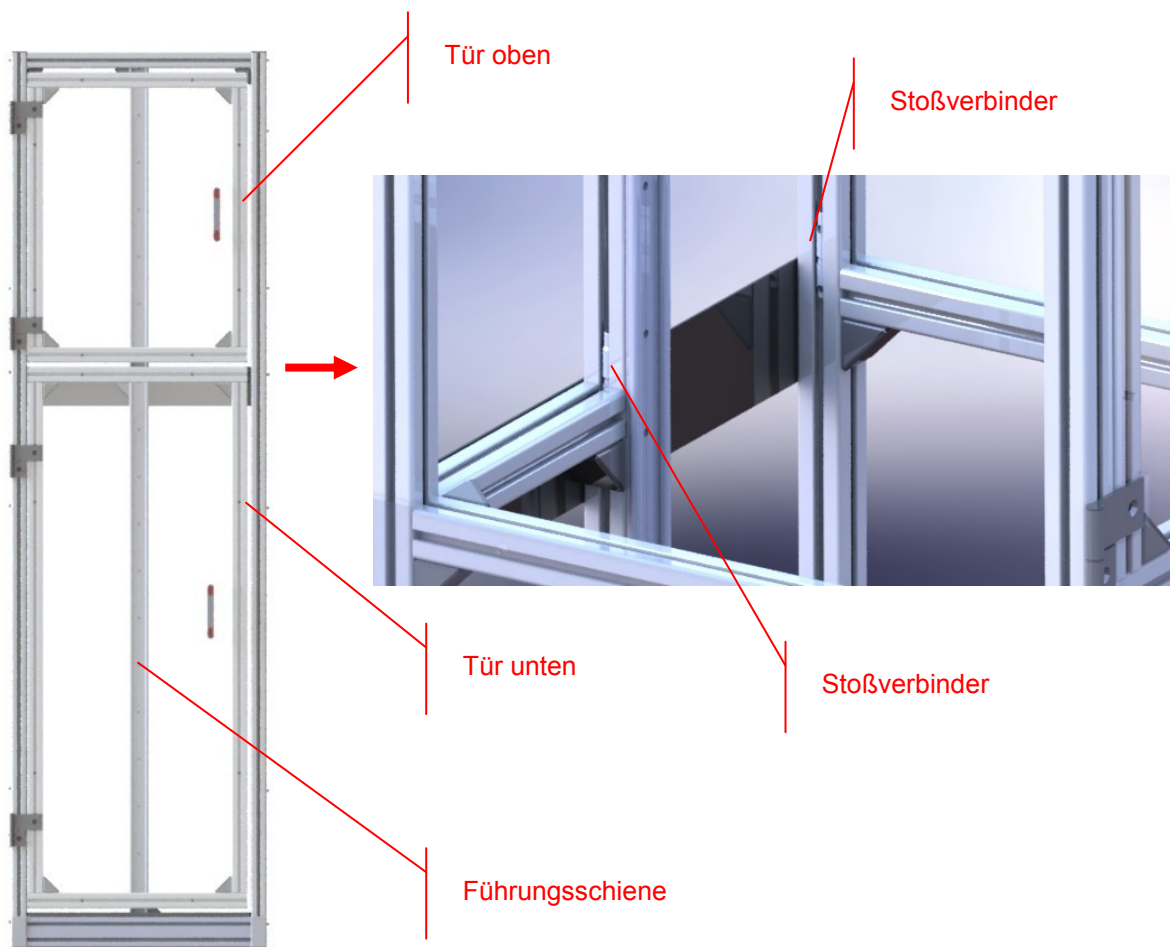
Rahmenaufbau des Prüfgerätes mit Detailansicht der Stoßverbinder. Quelle: Eigene Darstellung
